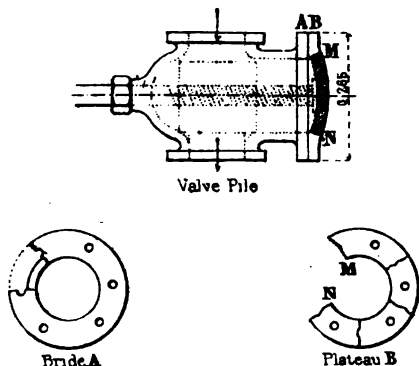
, 22 et 23. — Valve d'admission de vapeur à une machine, rompue à Tourcoing (valve F de la fig. 20).
